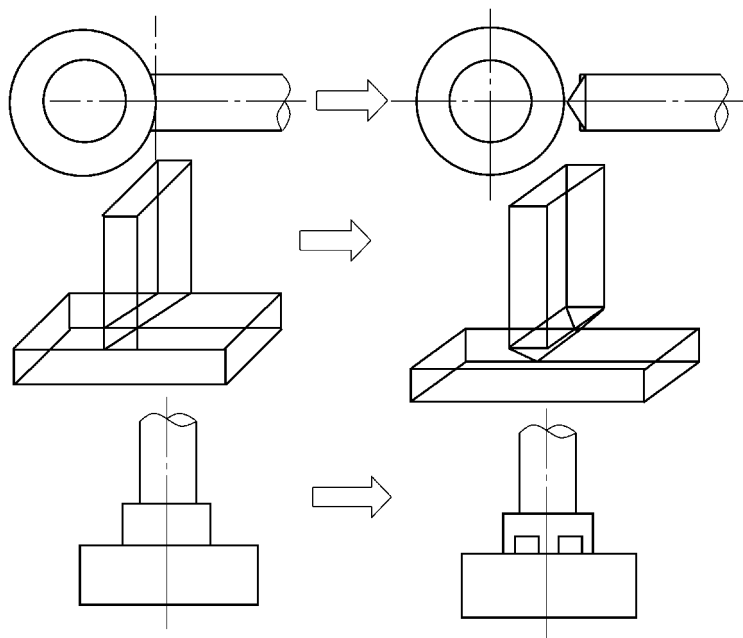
焊区体积较大时的凸焊接头处理
